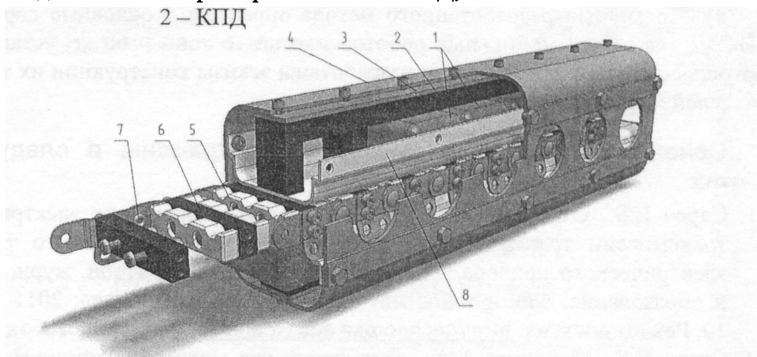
Устройство ЛВИТЭД и гусеницы-ротора для мобильного робота:
